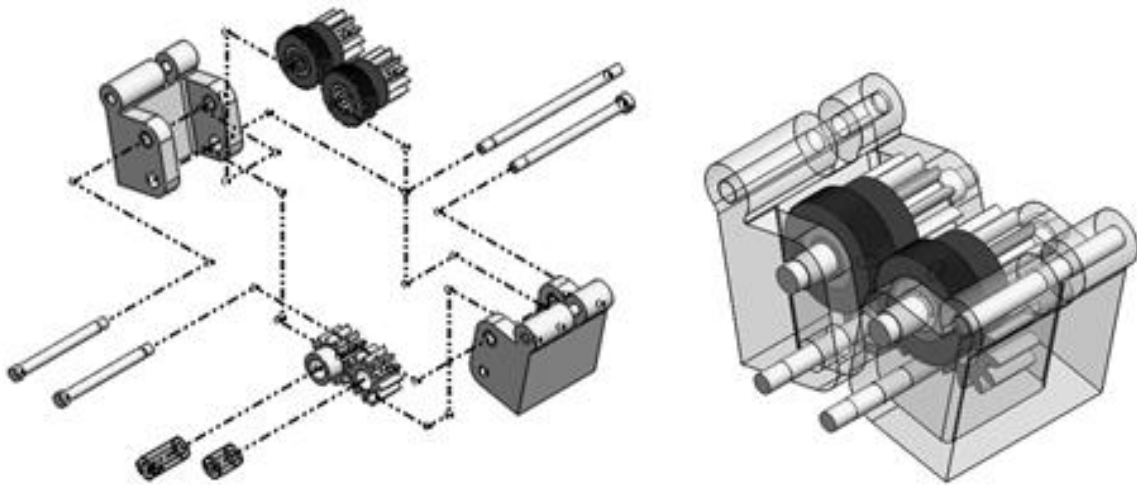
Montaje del sistema de engranajes sobre sus soportes
